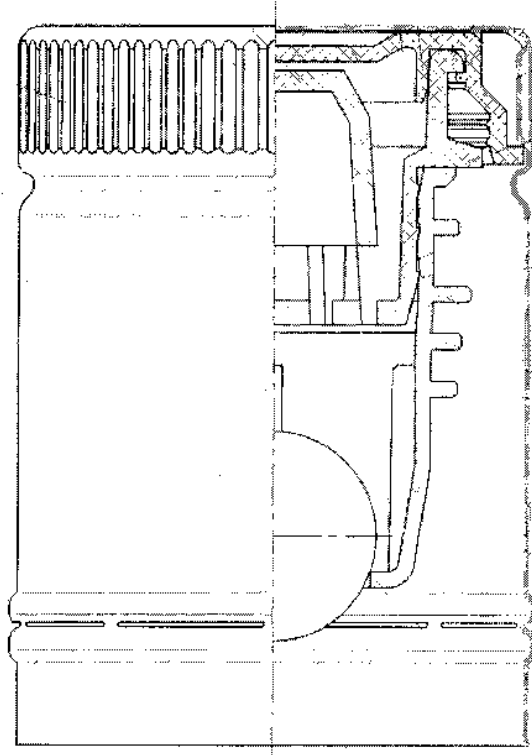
Схема закупорювального пристрою для пляшки з рідиною
